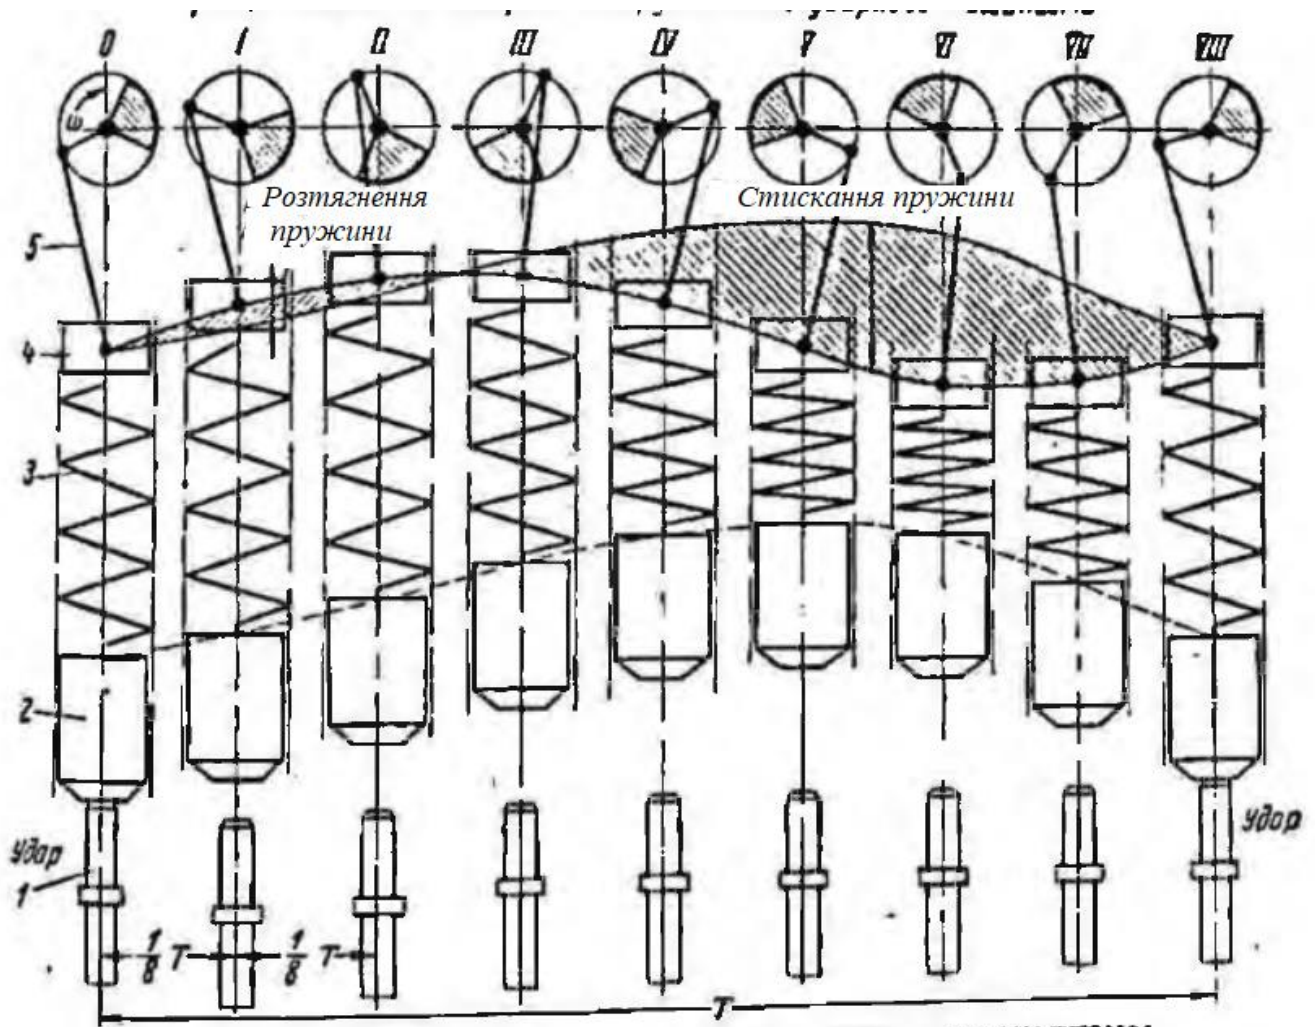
Схема роботи пружинного ударного механізму [13]: 1 – інструмент; 2 - бойок; 3 - пружина; 4 - повзун; 5 - шатун
